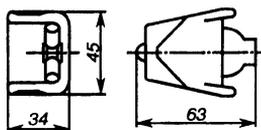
Замок крепления оттяжки в верхней части опоры
